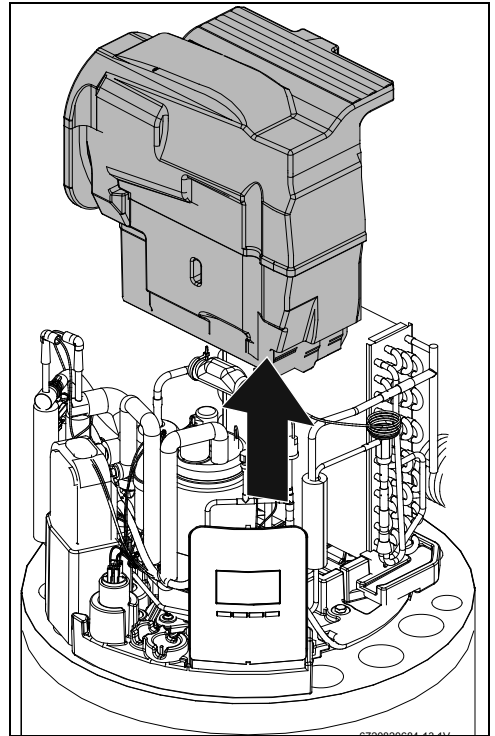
Baugruppe Luftführung und Gebläse entfernen.
